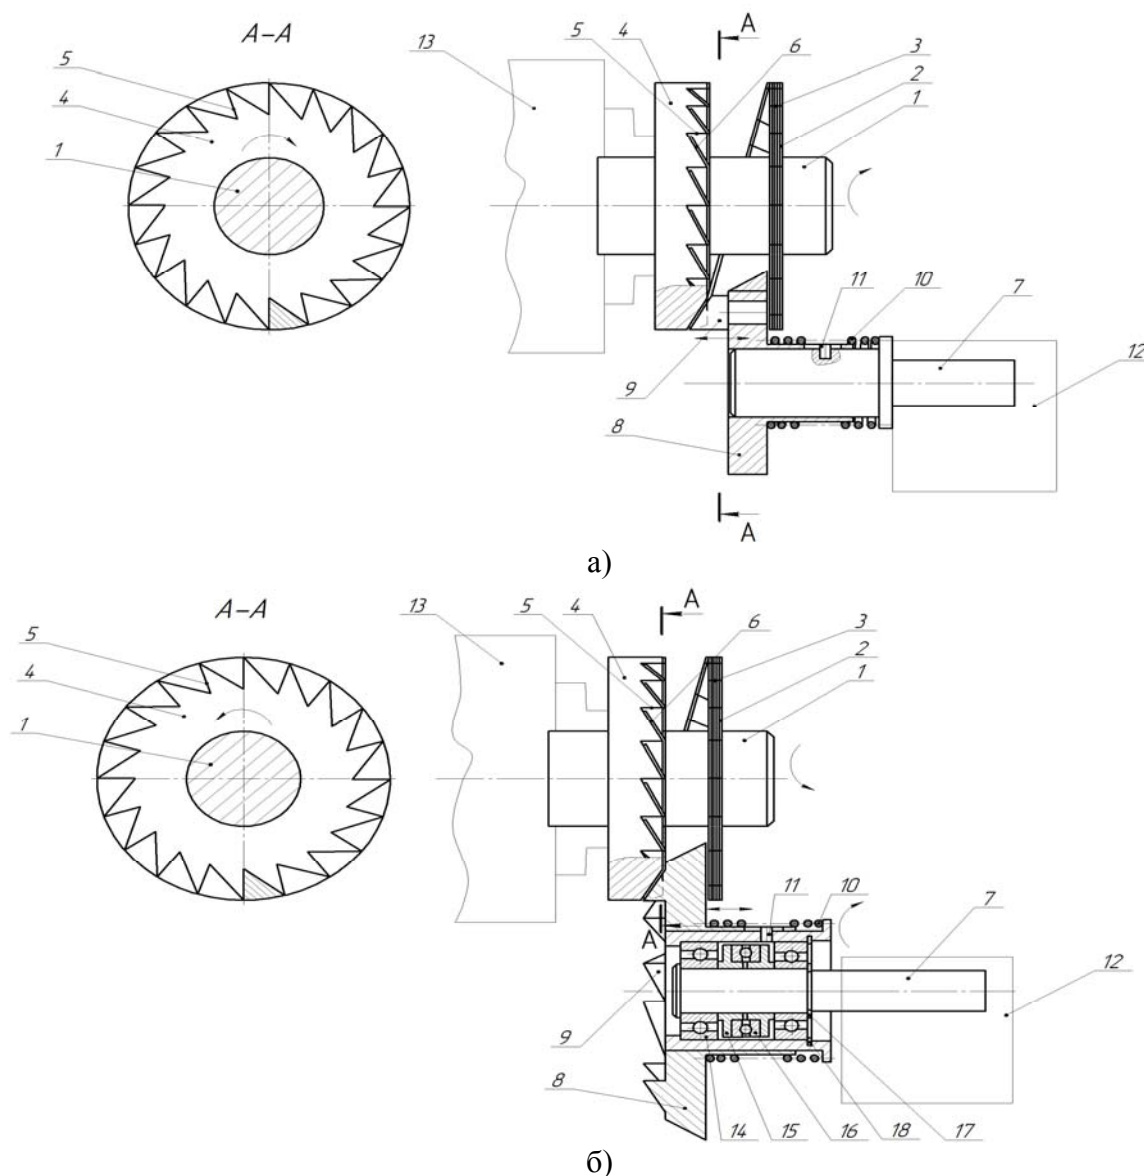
Пристрої для виготовлення лопатевих спіралей передбачає виконання
